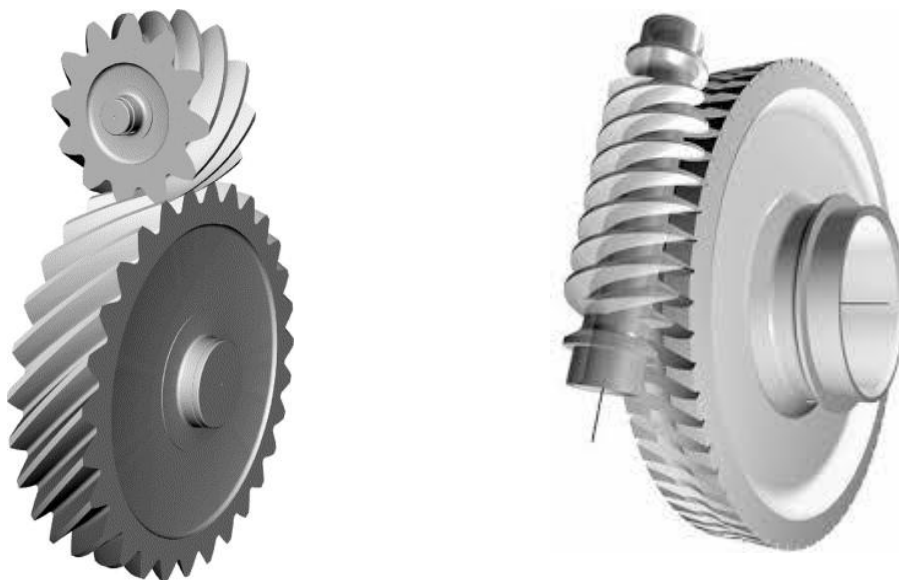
Engrenagem cruzada helicoidal, em oposição a um engrenamento parafuso sem-fim e roda dentada.
